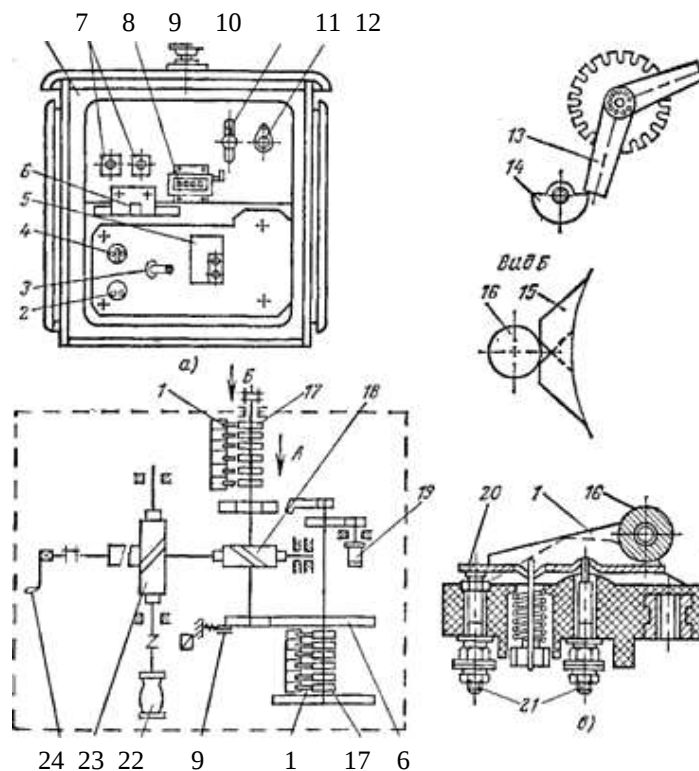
Привод типу ПДП-4У: а - вид на панель управління; б - кінематична схема; в - кулачковий елемент у розрізі; 1 - кулачковий елемент; 2 - розетка штепсельна; 3 - перемикач; 4 - вмикач обігріву; 5 - вимикач автоматичний, 6 - показчик положень; 7 - корпус привода; 8 - пости керування; 9 - лічильник числа перемикачів; 10 - вихідний вал; 11 - ручне блокування; 12 - лампа сигнальна; 13 - упор регульований; 14 - упор; 15 - виступ кулачковою шайби; 16 - ролик, 17 - шайба кулачкова; 18 - другий ступінь редуктора; 19 - сельсин; 20 - контакт рухливий; 21 - контакт нерухомий, 22 - електродвигун, 23 - перший ступінь редуктора; 24 - ручка приводу.
